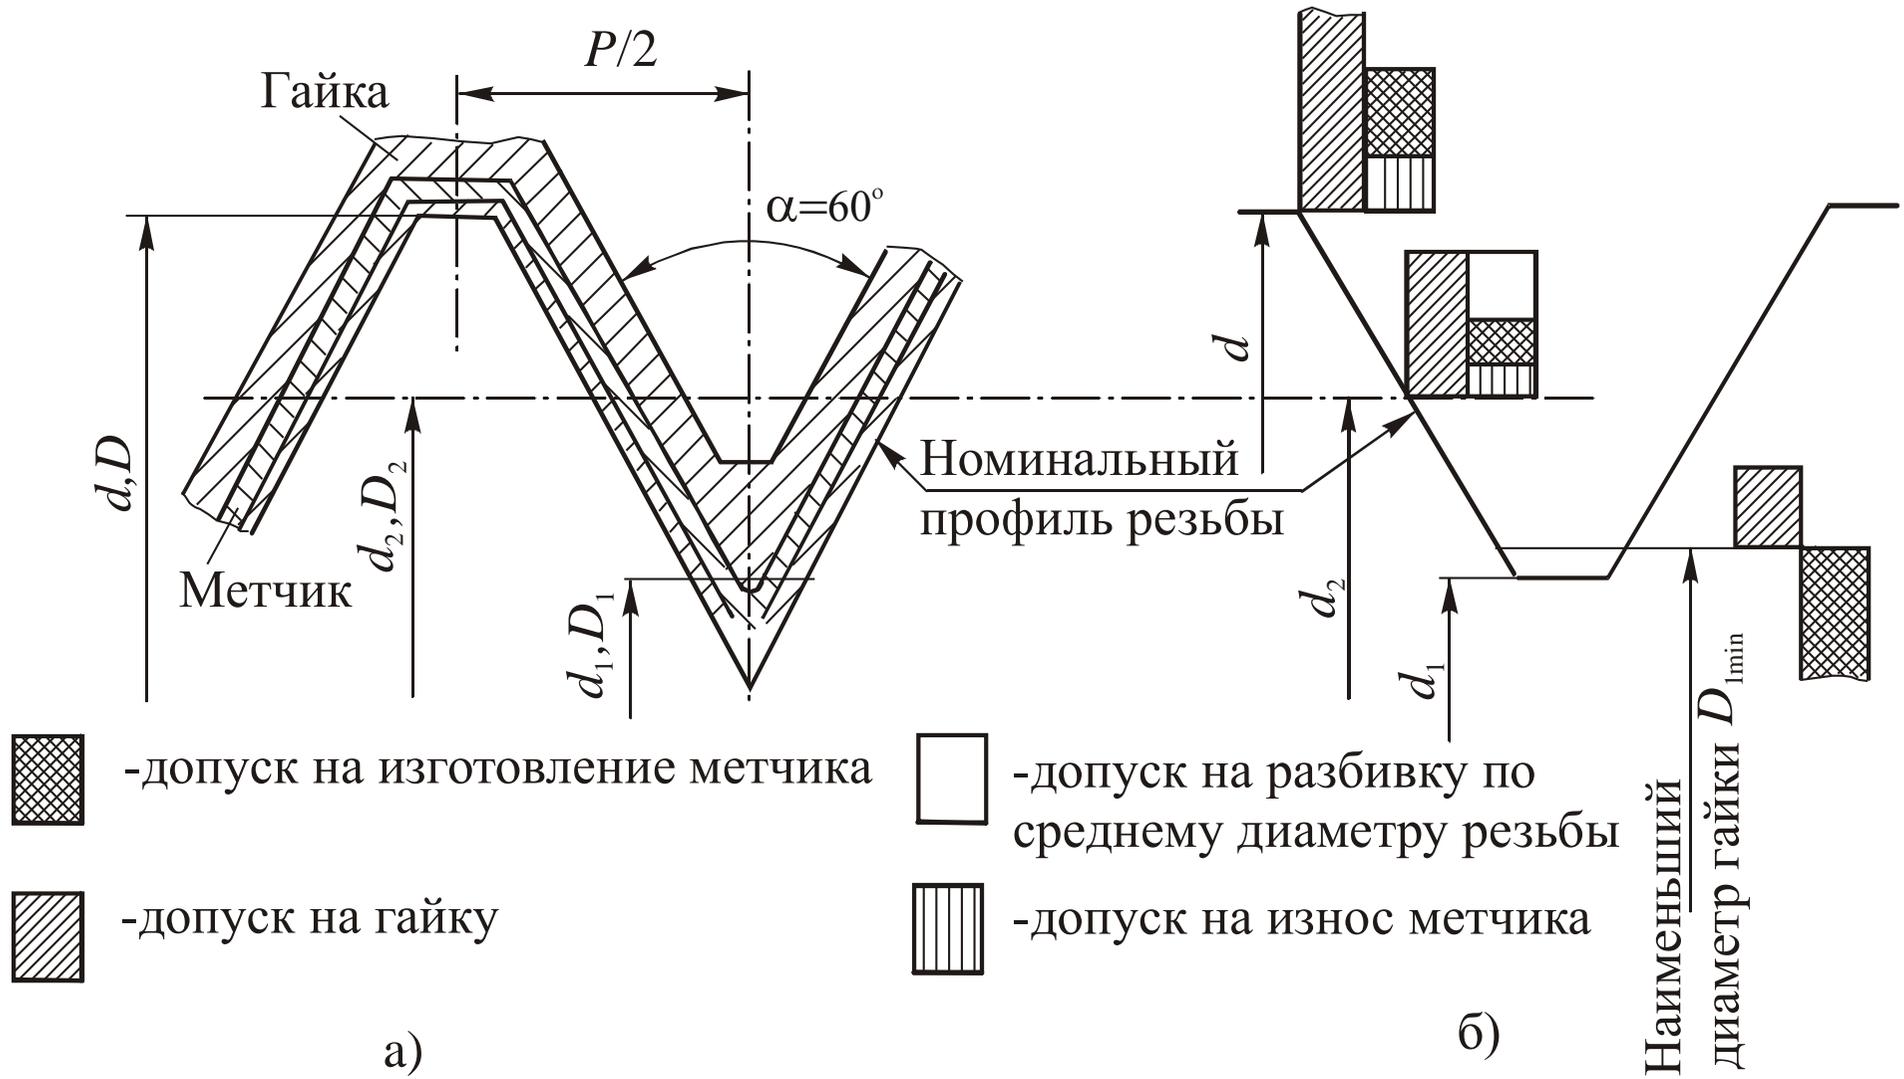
Схемы расположения полей допусков на диаметры резьбы метчика (d , d_1 , d_2) и гайки
